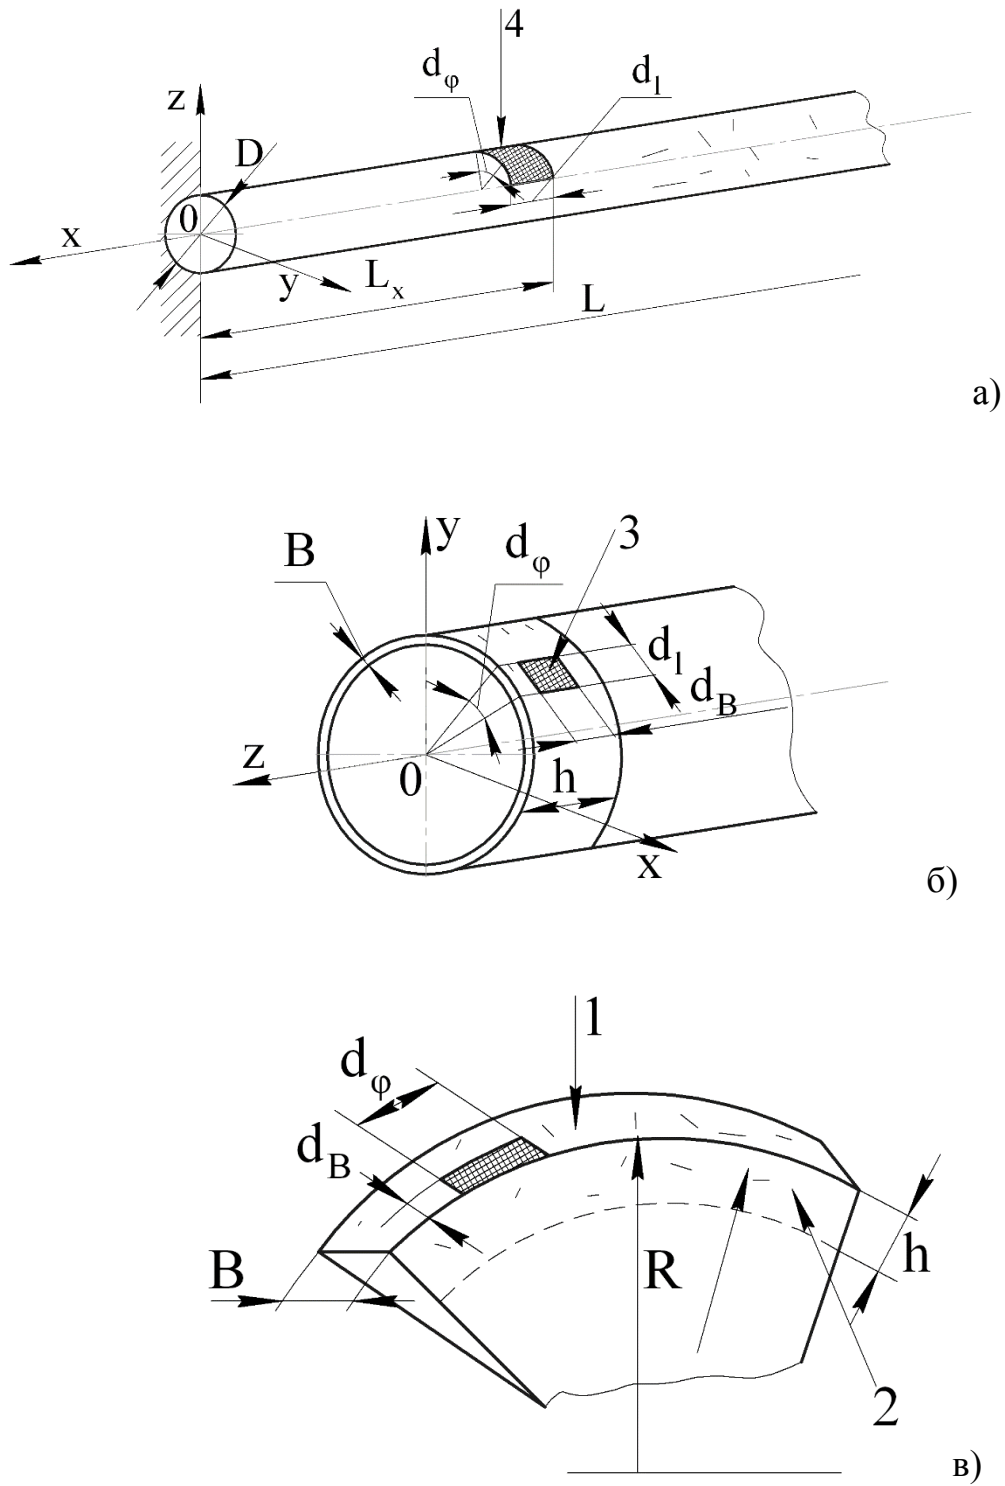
Розрахункові схеми нагрівання елементів поверхонь типових виробів: а) алмазної струни; б) кільцевого свердла; в) торця круга
